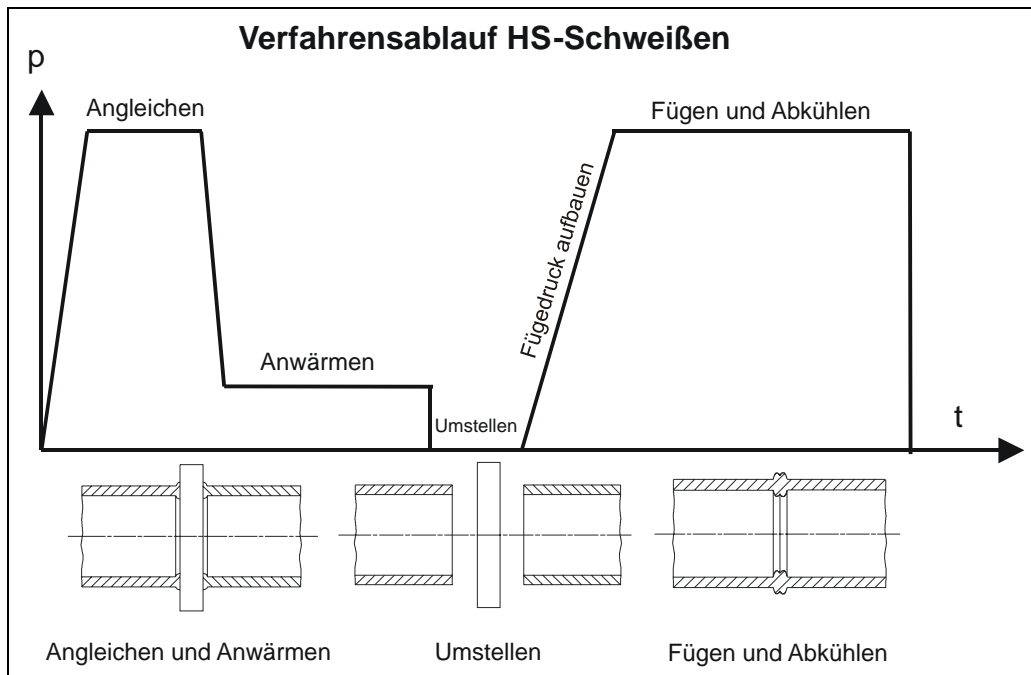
Ablaufschema des Schweißvorganges (HS-Schweißen)
